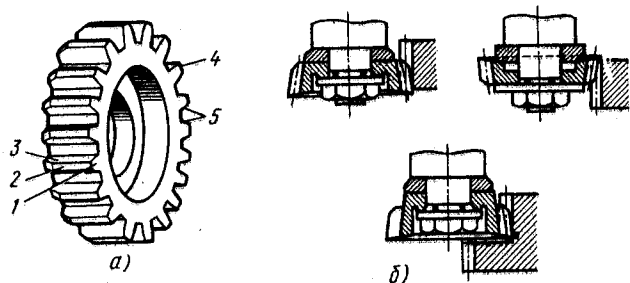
Конструктивные элементы зуборезного долбяка (а) и схемы его установки (б)
